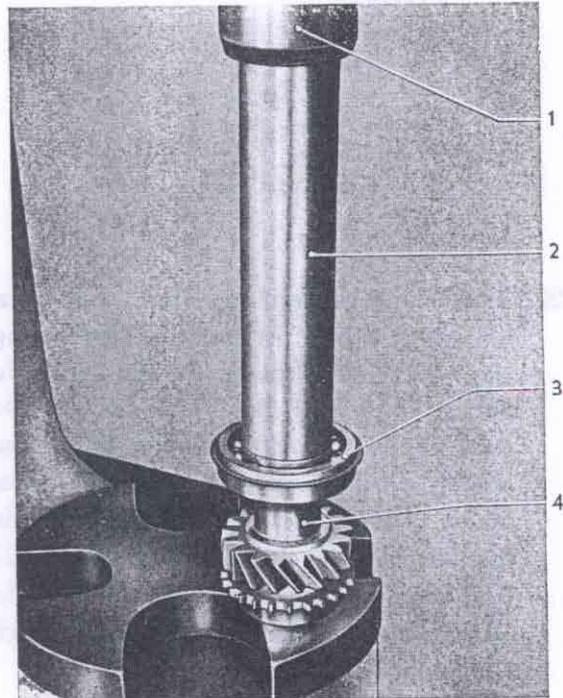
Kugellager auf Hauptantriebrad aufpressen
